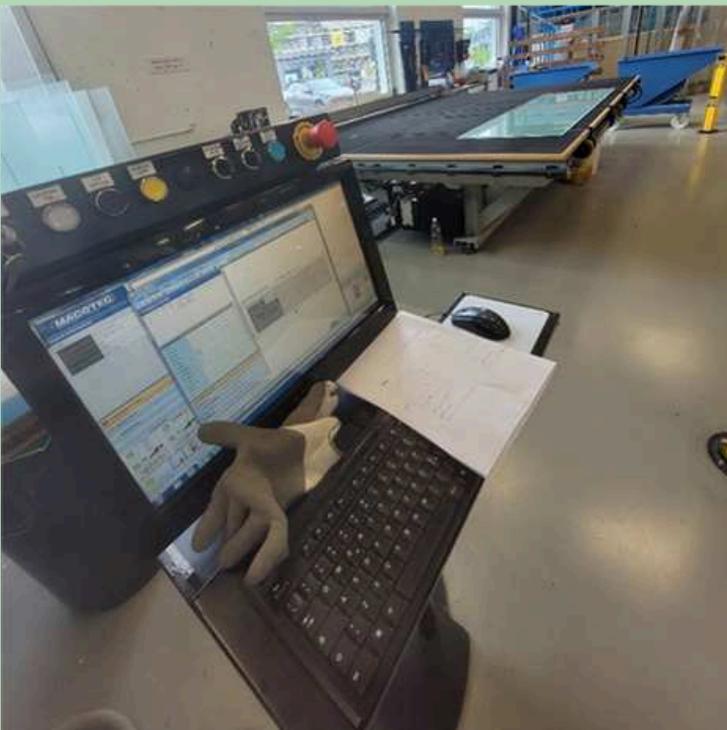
CNC-Bearbeitung mit 5 mm Zugabe pro Kante
